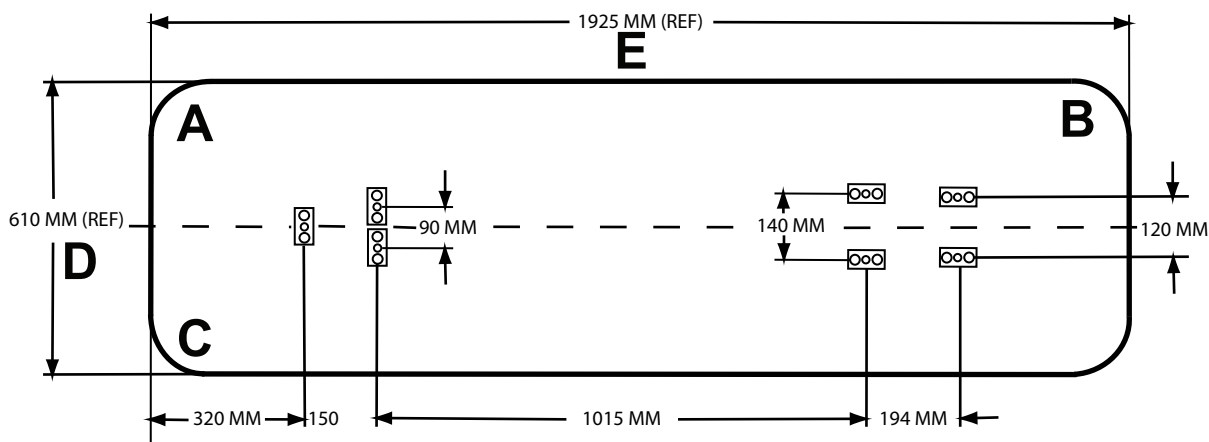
Posizioni per l'installazione delle piastre a pavimento
